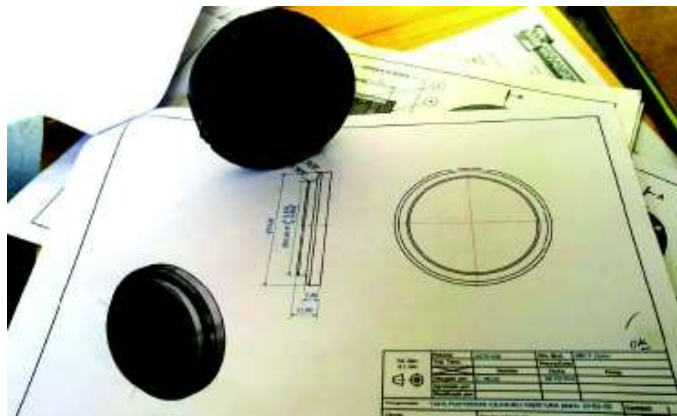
Material base y plano a detalle de las tapas posteriores.
